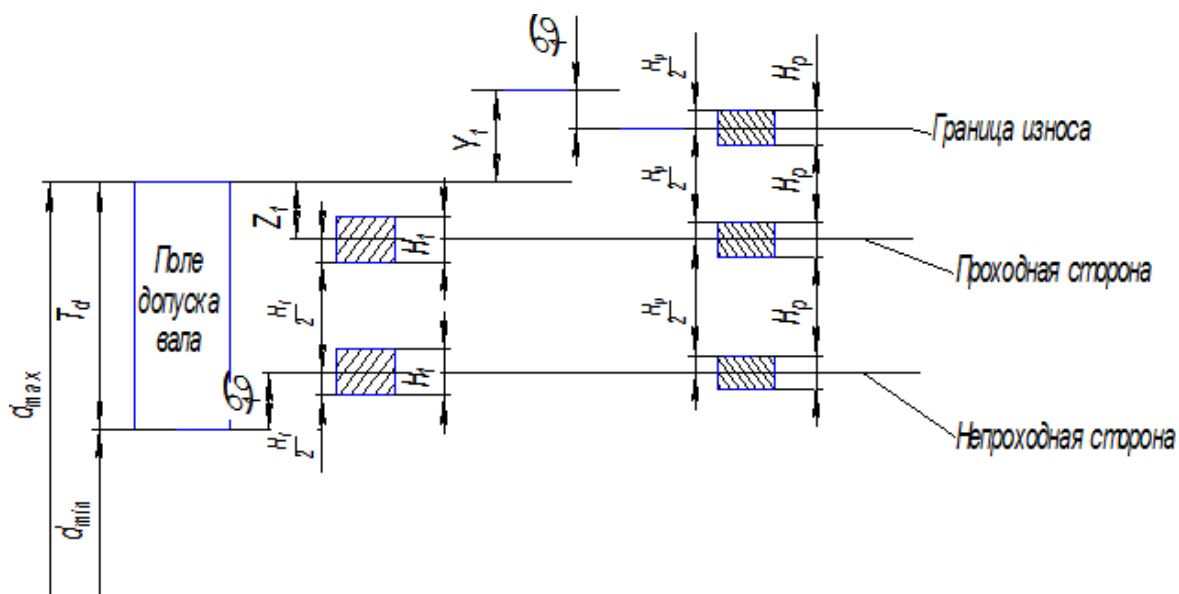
Схема расположения полей допусков калибров для контроля валов и контркалибров
